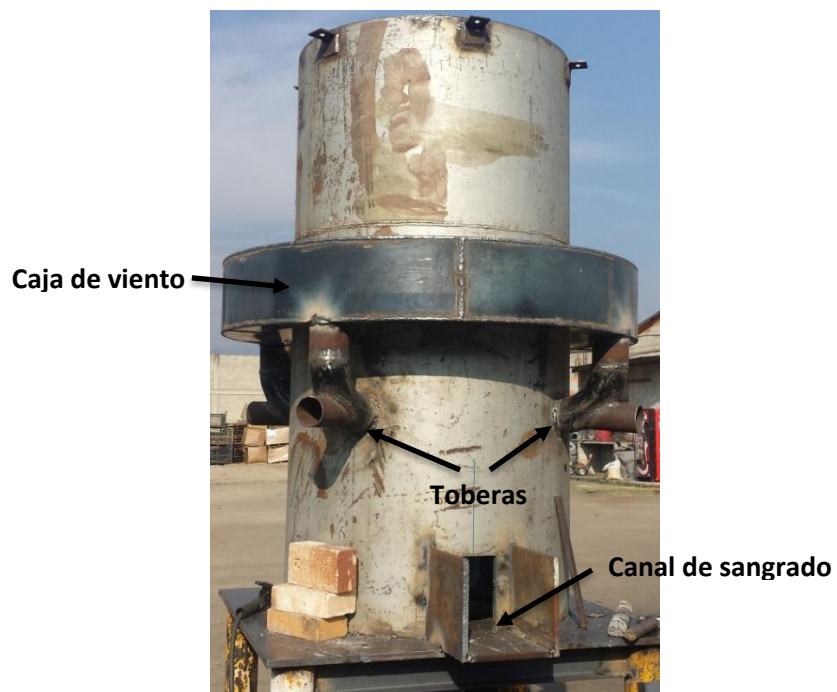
Construcción del área inferior de horno (canal de sangrado).
